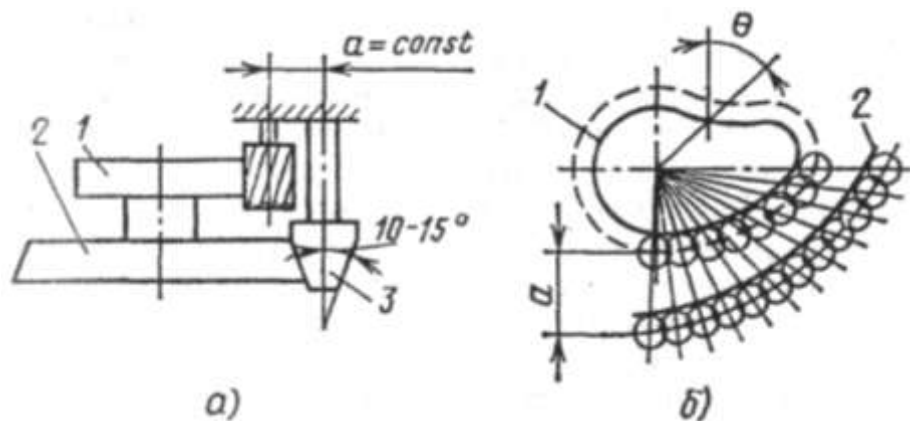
Примеры обработки по корпусу: а — схема фрезерования замкнутого контура методом круговой подачи; б — схема построения профиля копира для фрезерования сложного профиля детали
